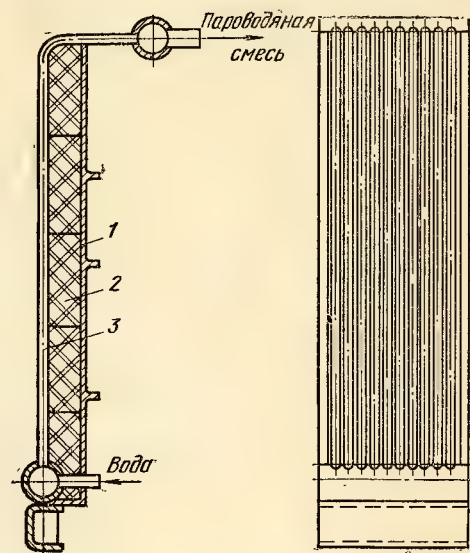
Трубчатый кессон шахтной печи: 1 — несущий газоплотный каркас; 2 — термонзолия; 3 — трубчатый экран
